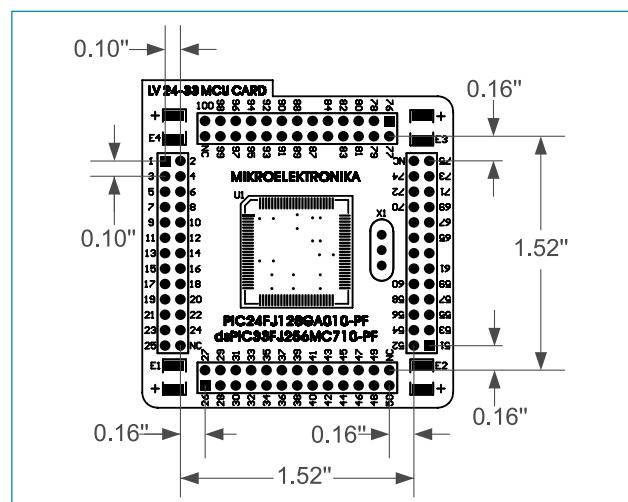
Dimensiones de la tarjeta MCU para las *MCU Card 1* a *MCU Card 8
